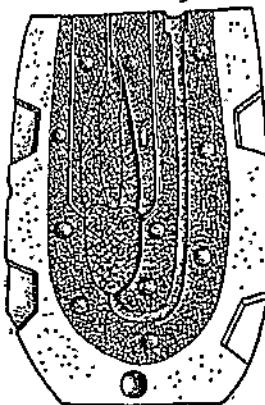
Отливка „под давлением“. Австралийский каменный нож. Передняя половина формы.
